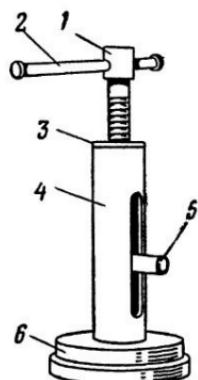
Модель винтового механизма: 1 — винт; 2 — ручка; 3 — гайка; 4 — труба; 5 — стопор; 6 — основание.
